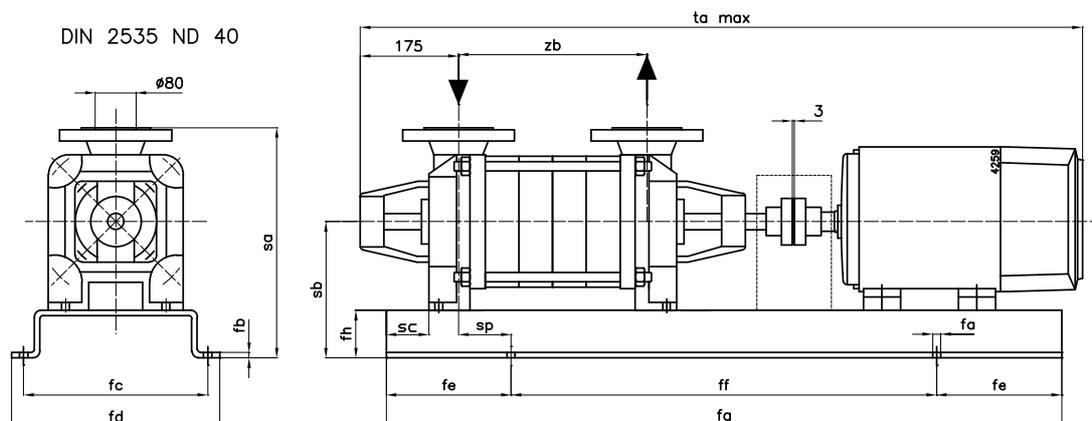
Dimensioni pompa con motore MCHZ(S) 20b.
